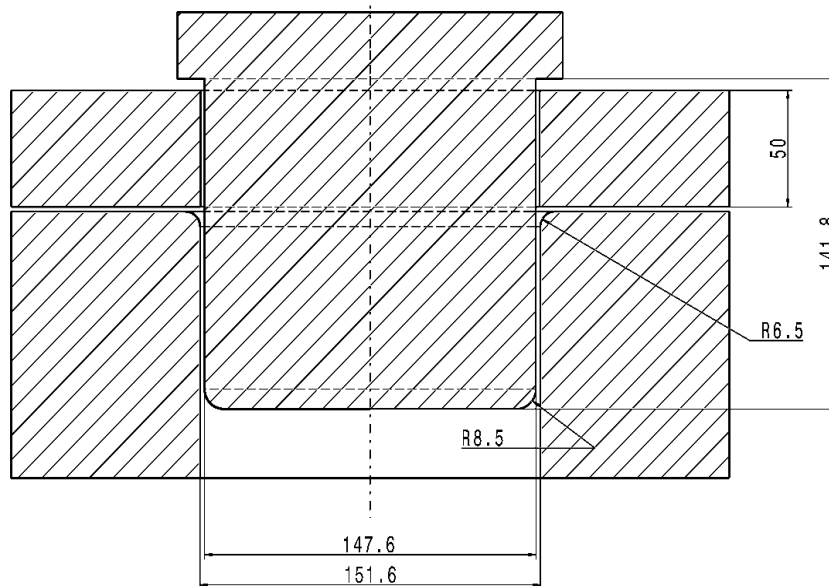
Geometrie des Napfziehwerkzeuges
